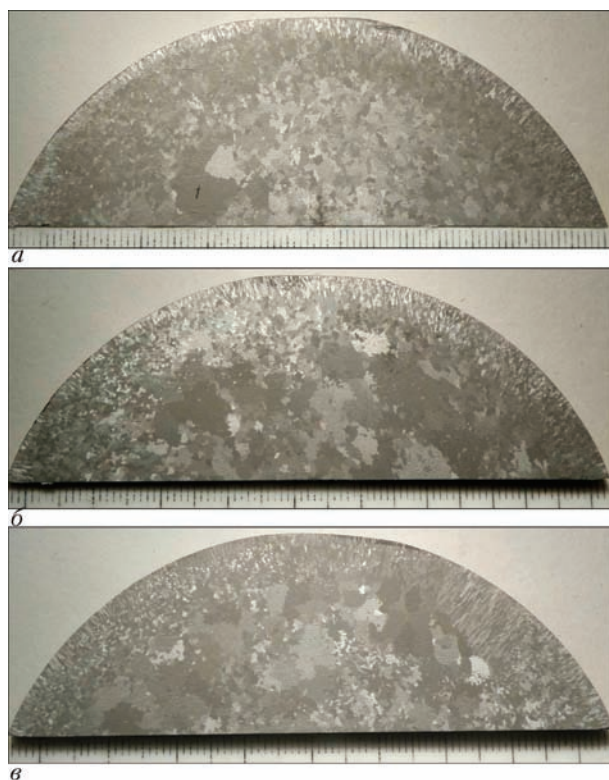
Макроструктура в поперечном сечении заготовки диаметром 97 мм, полученной из возврата сплава ЖС26-ВИ способом ЭЛП: *а* — верх; *б* — середина; *в* — низ
